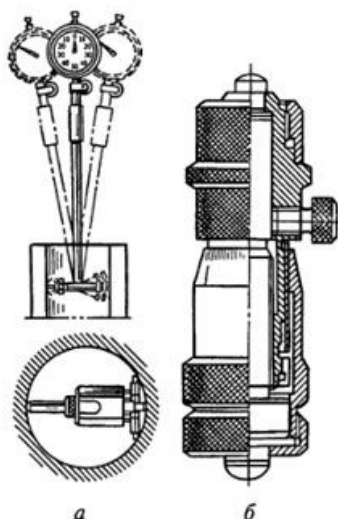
Нутромеры: а – индикаторный; б – микрометрический
